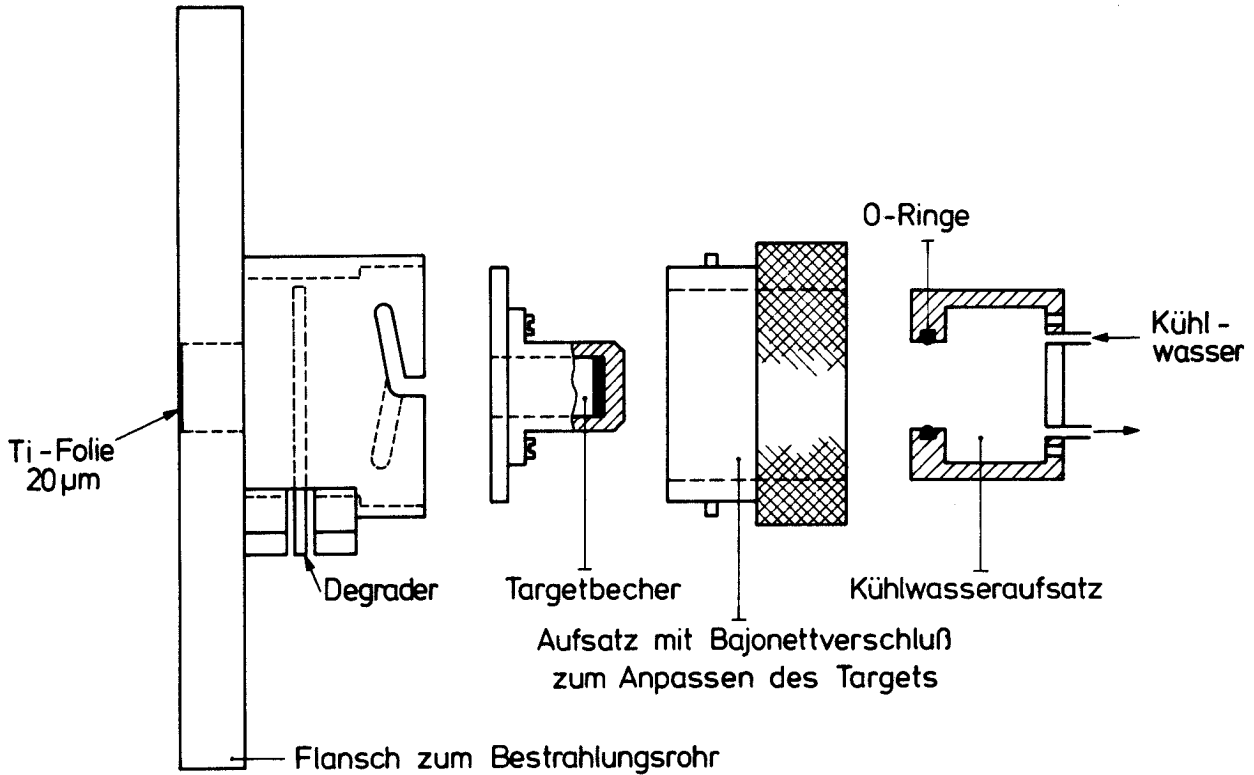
Explosionszeichnung des wassergekühlten Targets
